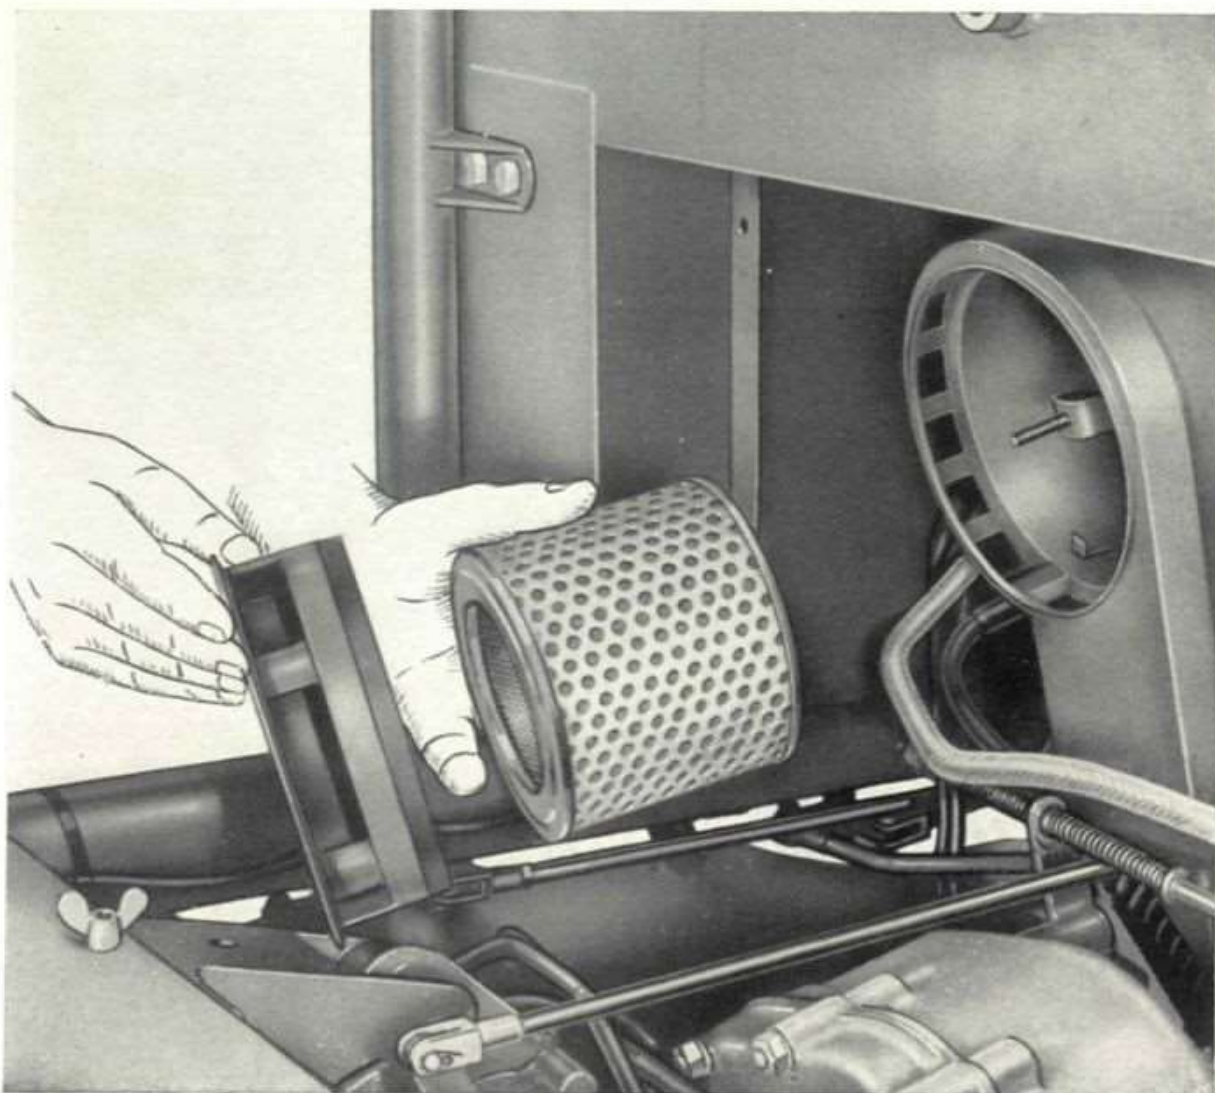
Come viene smontato il filtro dell'aria per il carburatore.
